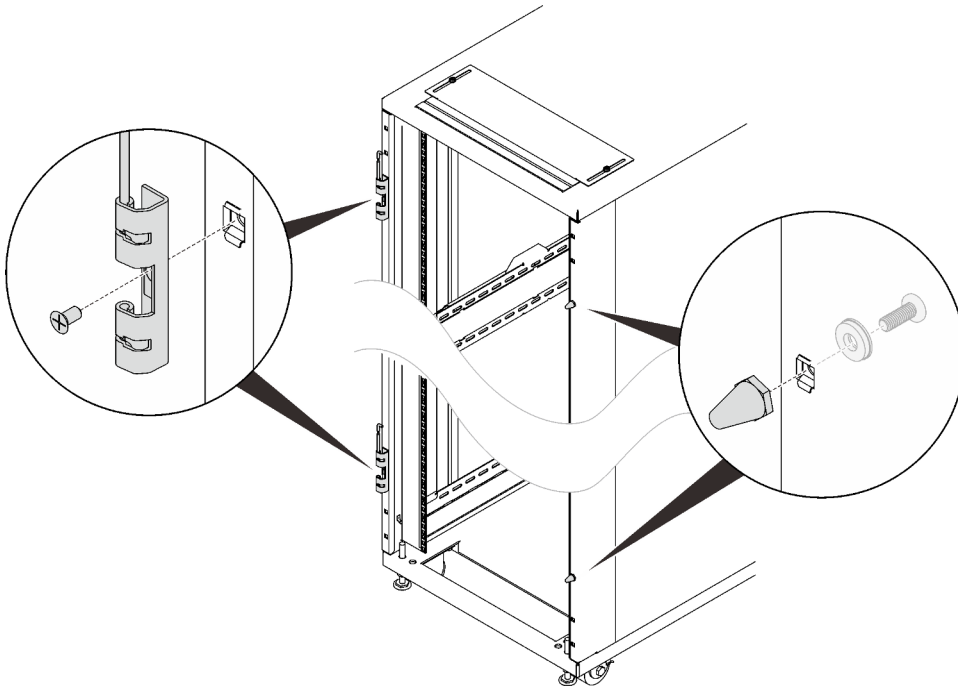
Extracción de las bisagras de la puerta y las cubiertas inferiores de extensión
